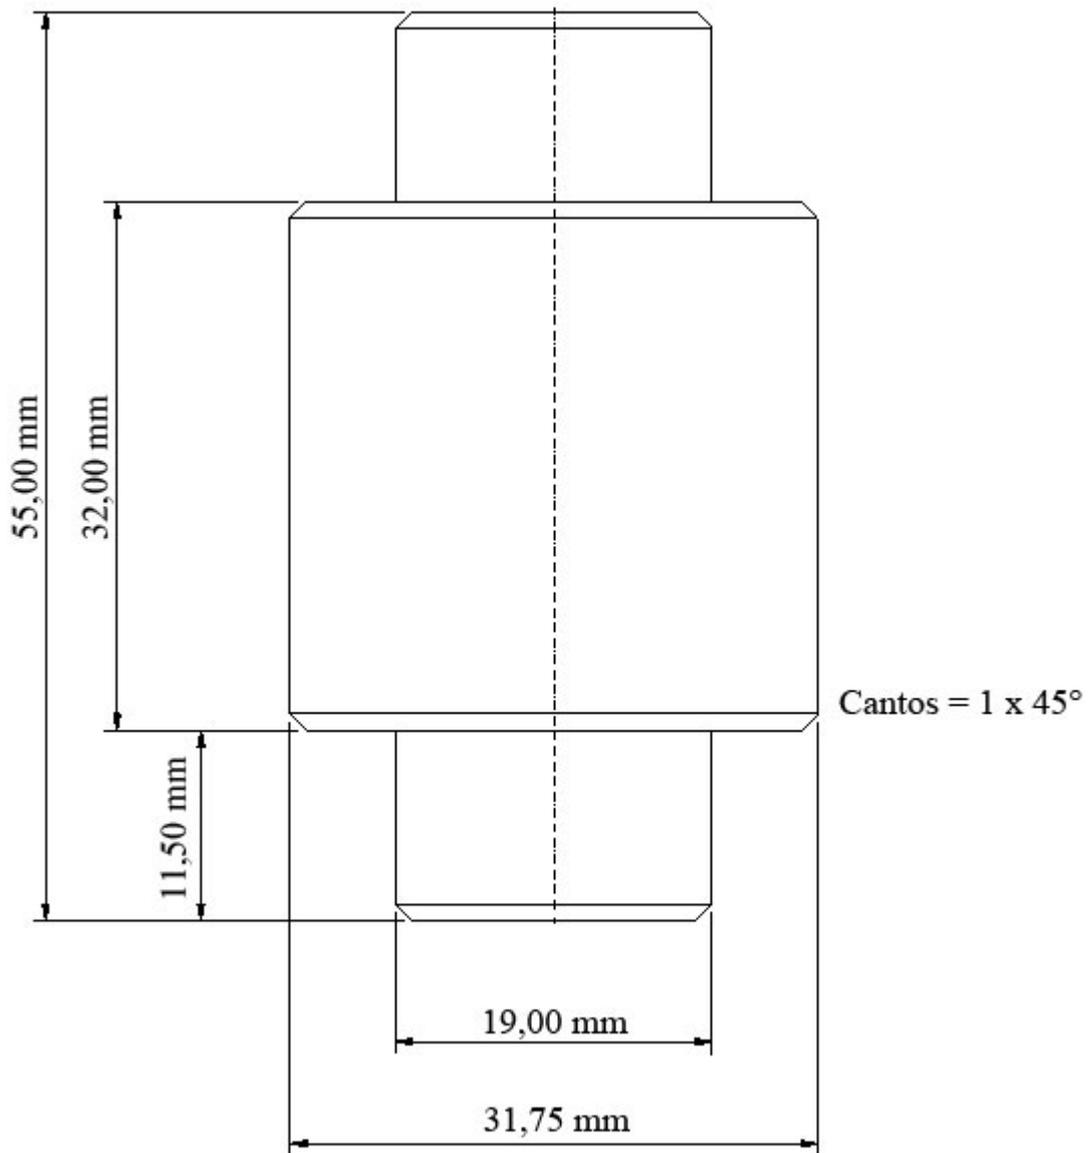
DESENHO TÉCNICO – ESPECIFICAÇÕES DE ENGENHARIA
